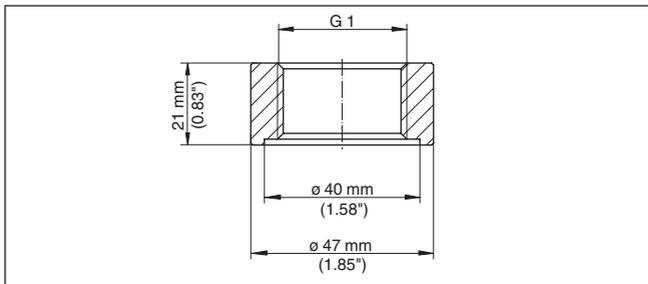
medidas da luva para soldagem G1 (DIN 3852-X)
